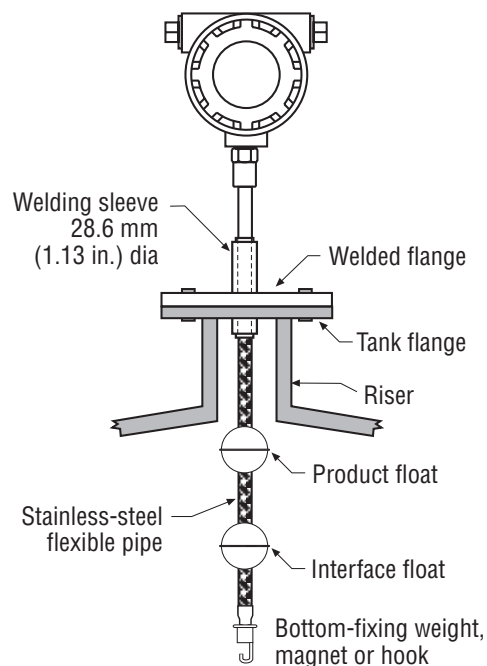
Montagem com conexão soldada para haste rígida e flexível
